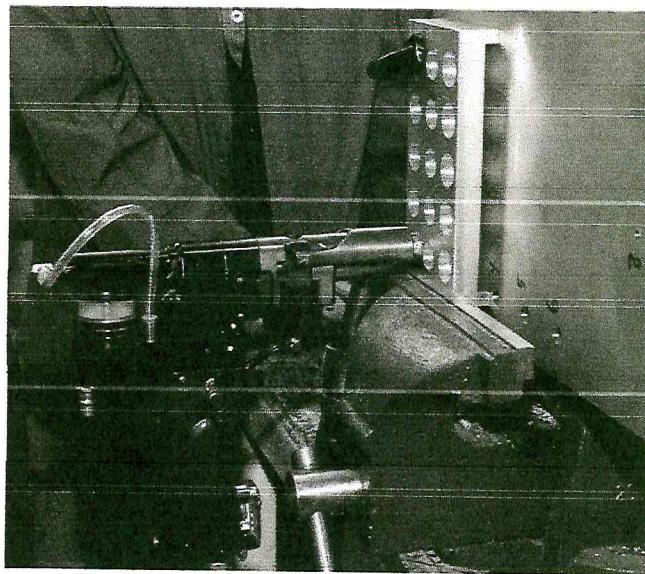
Фиксация СМАП на обрабатываемой поверхности с помощью кондуктора
